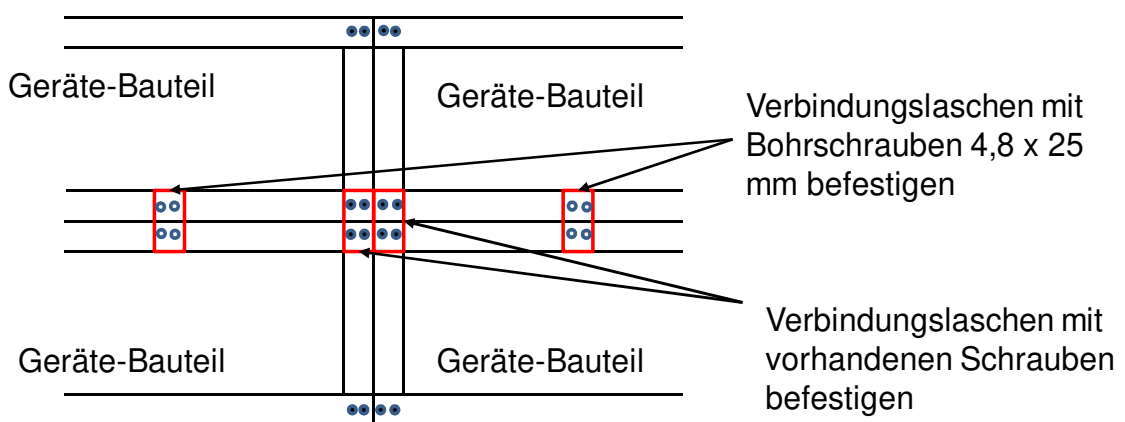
Darstellung der horizontalen Bauteilverbindung
